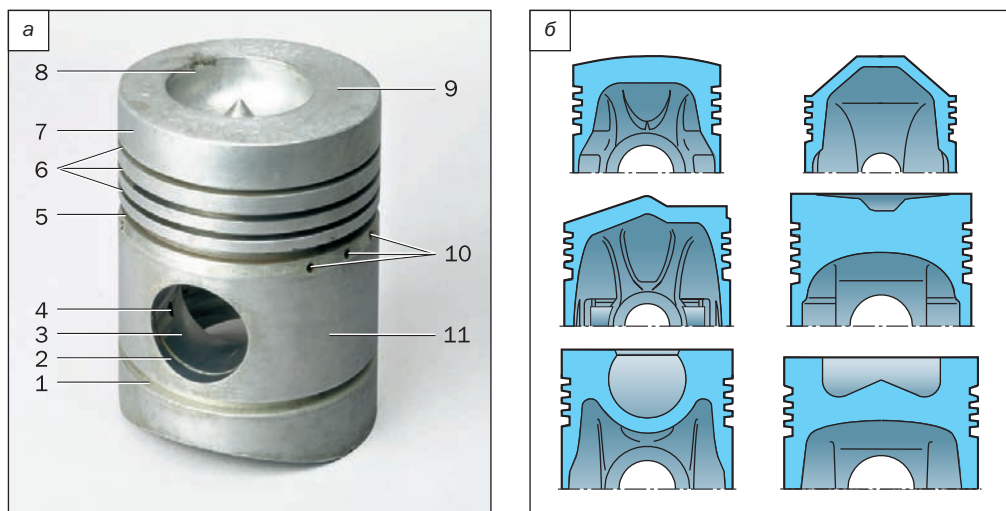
Поршень дизельного двигателя (а) грузового автомобиля и формы поршней разных двигателей (б): 1 — канавка нижнего маслосъемного кольца; 2 — проточка под стопорное кольцо поршневого пальца; 3 — внутренняя поверхность бобышки; 4 — отверстие для смазки поршневого пальца; 5 — канавка верхнего маслосъемного кольца; 6 — канавки компрессионных колец; 7 — головка поршня; 8 — камера сгорания в поршне; 9 — днище поршня; 10 — отверстия для отвода масла; 11 — юбка
